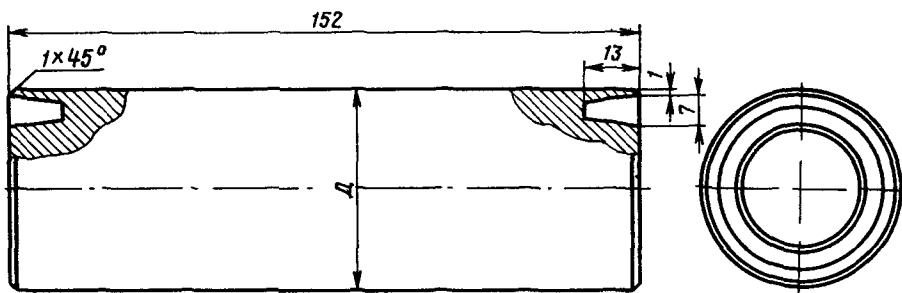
Балластный валик для запрессовки в палец поршня варианта 14В дизеля типа Д100
